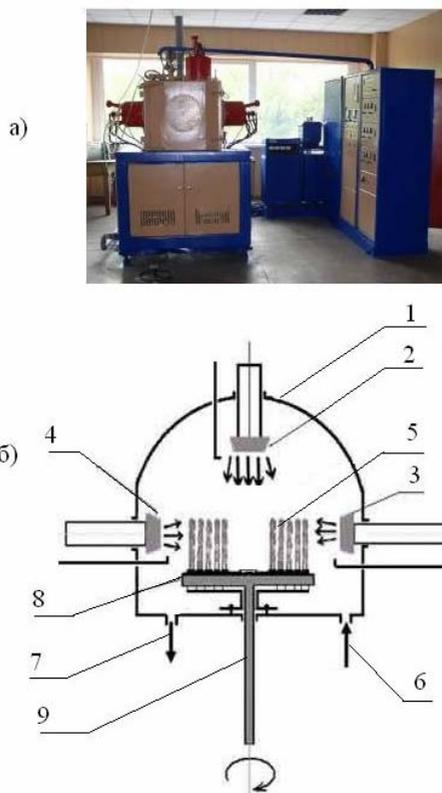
Внешний вид (а) и схема (б) установки ННВ-6.6-И1:
